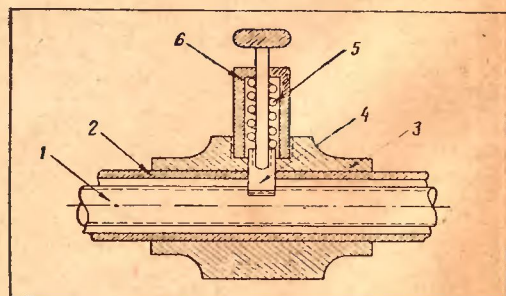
Устройство смещения с трубчатой направляющей; ходовой винт находится внутри направляющей. 1 — ходовой винт; 2 — направляющая; 3 — ползун; 4 — зубчатая гребенка; 5 — пружина гребенки; 6 — обойма пружины
